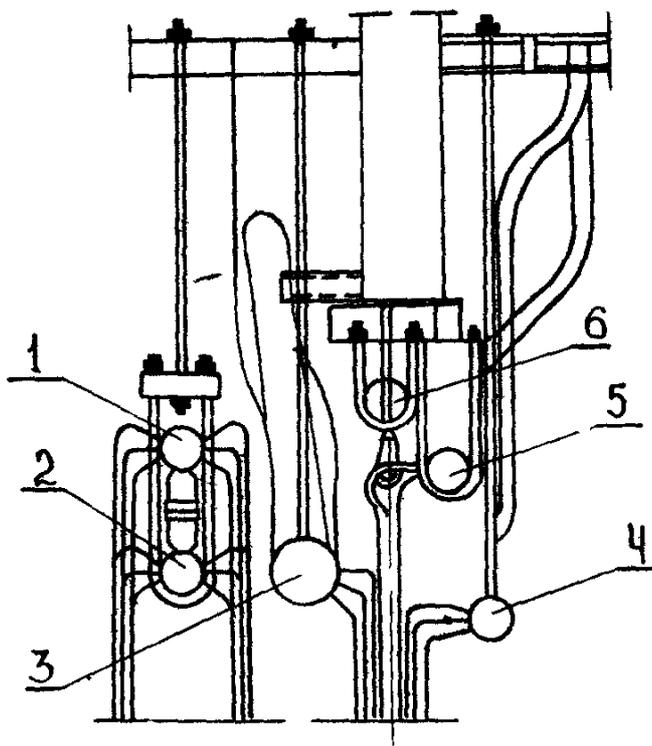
Подвеска камер первичного и вторичного пароперегревателя котла ТП 100
